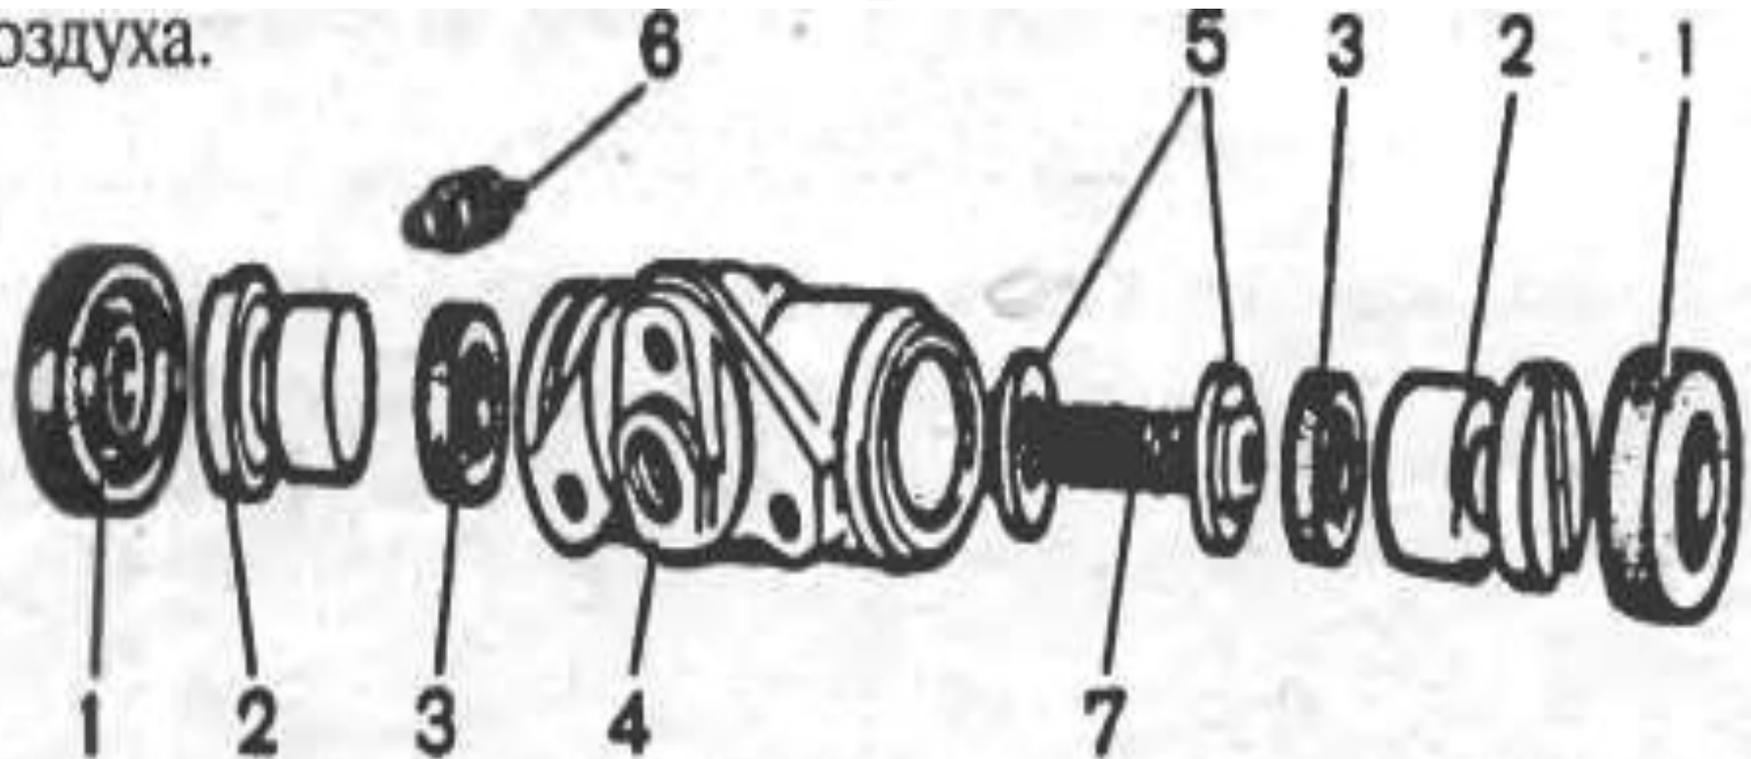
Детали колесного цилиндра: 1 - защитный колпачок; 2 - поршень; 3 - уплотнитель; 4 - корпус колесного цилиндра; 5 - чашки пружины; 6 - штуцер для прокачки привода тормоза; 7 - пружина
